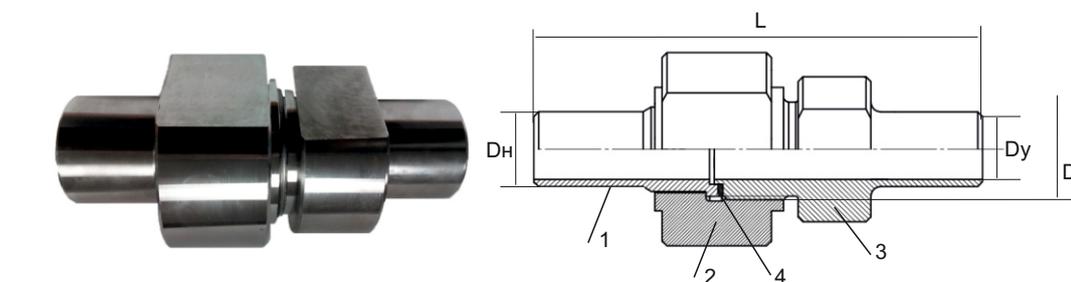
Ниппель для установки насадка на выпускном трубопроводе
